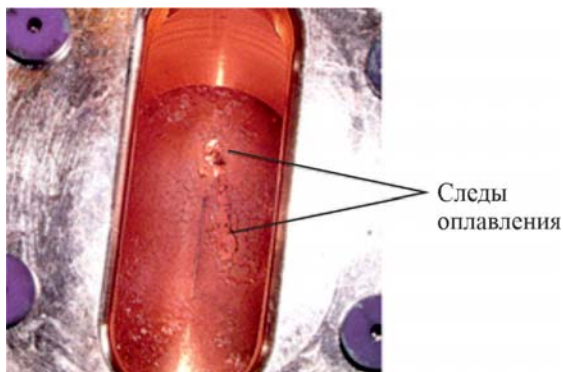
Фото внутренней поверхности базовой конструкции коллектора с оплавлением конусообразной поверхности
